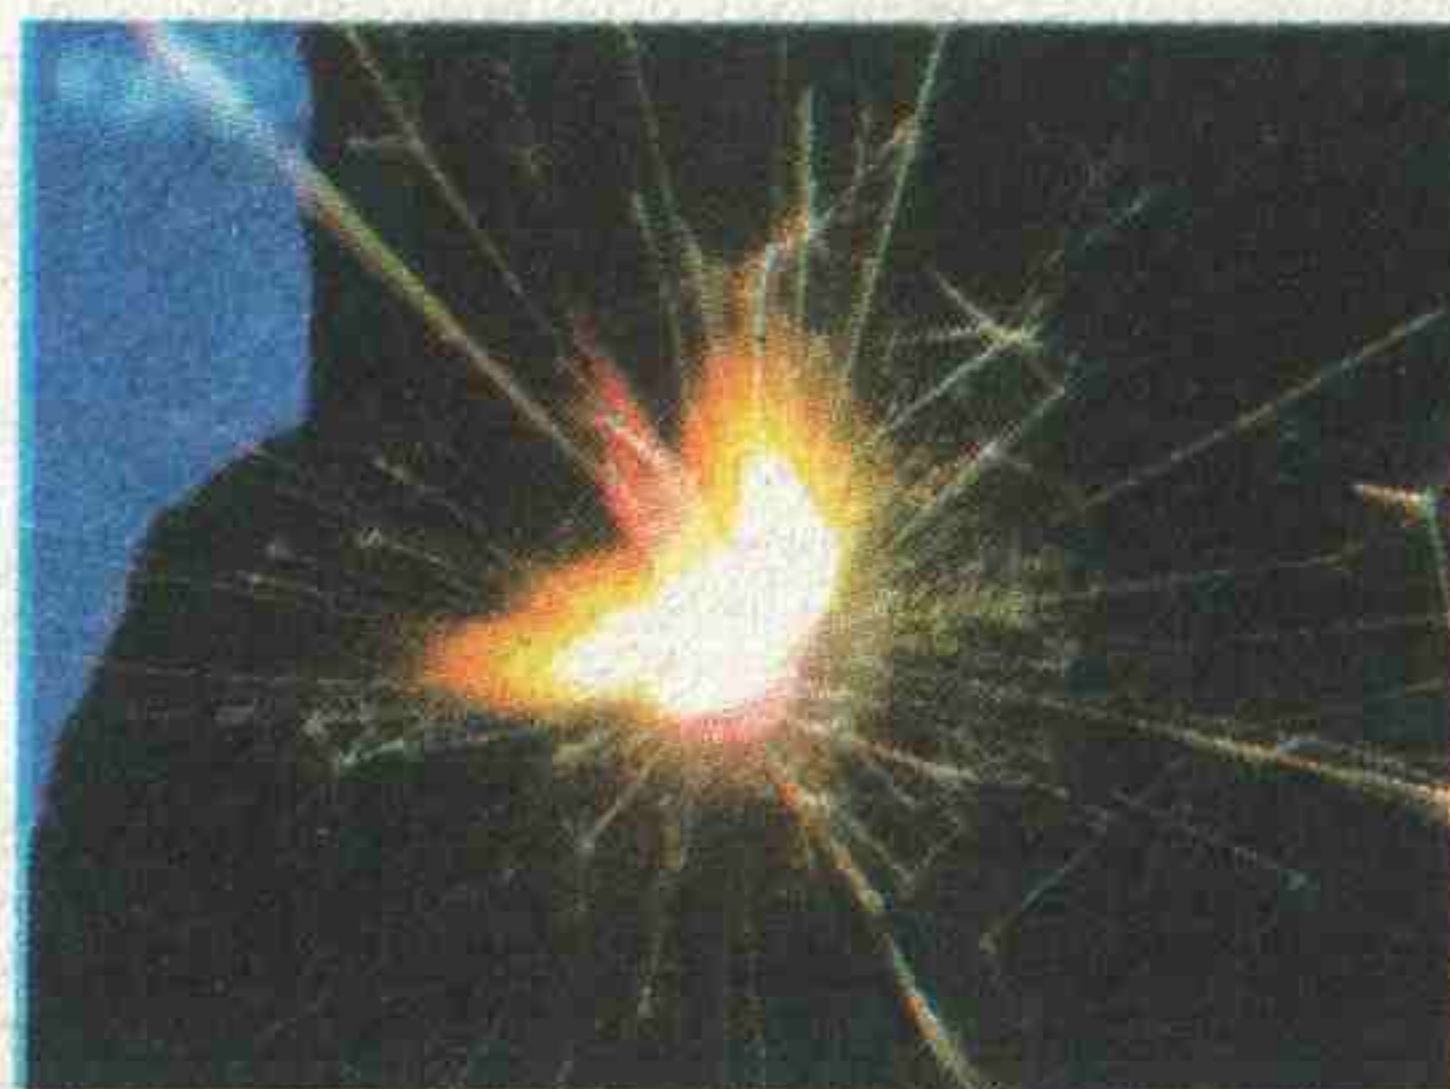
Сварка металла при помощи электрической дуги
